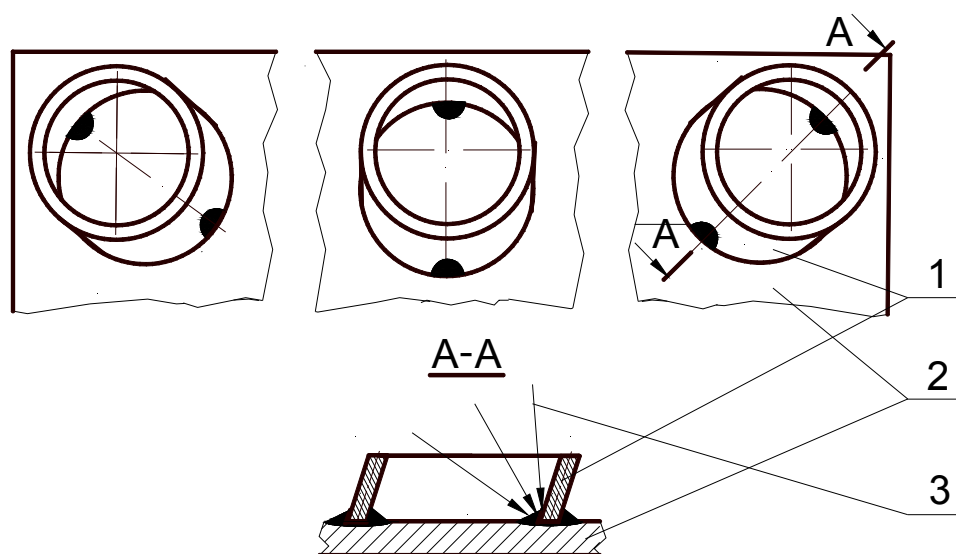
Розміщення та приспінання трубчатих утримуючих елементів до робочої пластини за допомогою лазерного приварювання.
